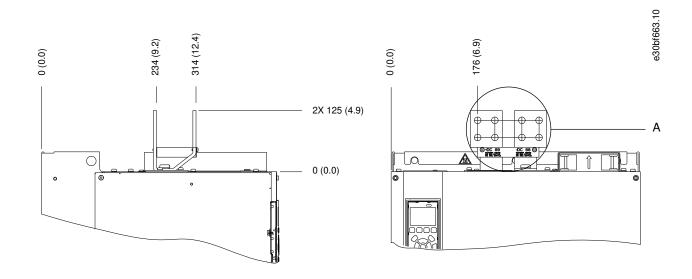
Dimensions des bornes réseau, moteur et de terre E3h (vues latérales)
